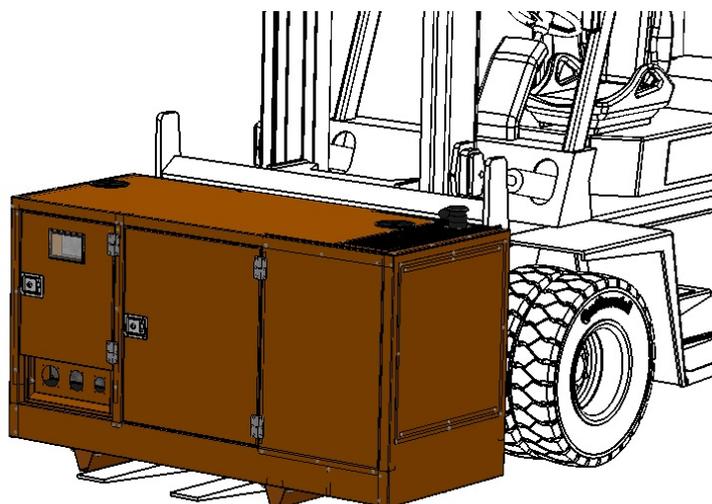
Izado con carretilla. Grupo insonorizado
